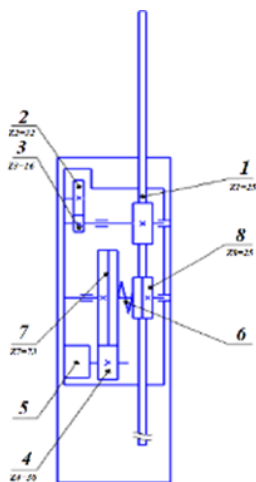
Схема кинематическая: 1 – рейка; 2 – зубчатое колесо; 3 – зубчатое колесо; 4 – зубчатое колесо; 5 – пружина; 6 – преобразователь перемещений; 7 – зубчатое колесо; 8 – вал-шестерня
